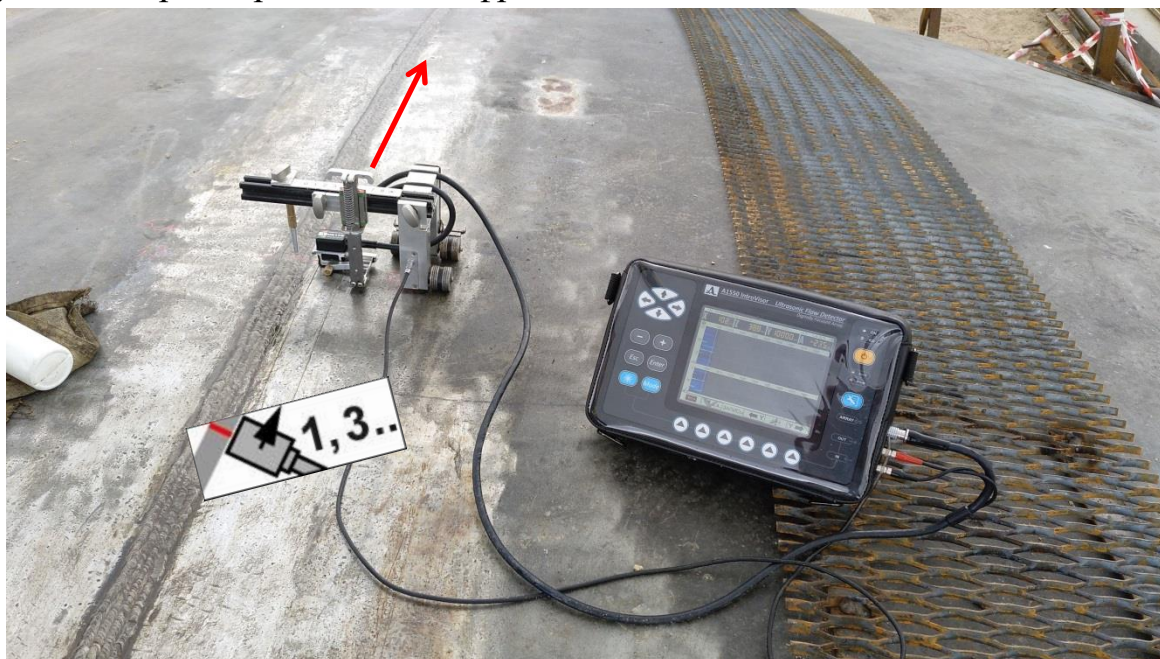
Фотография сварного соединения TANK-C39-40мм-09Г2С
